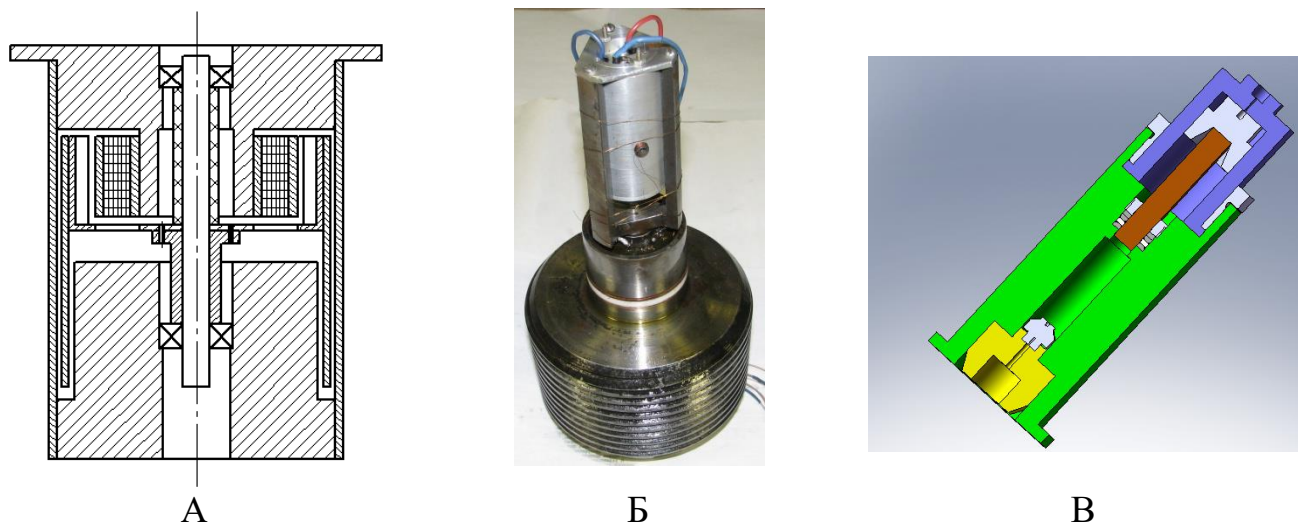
Конструкция (а) и внешний вид измерительной ячейки (б) и блок повышения давления (в)
